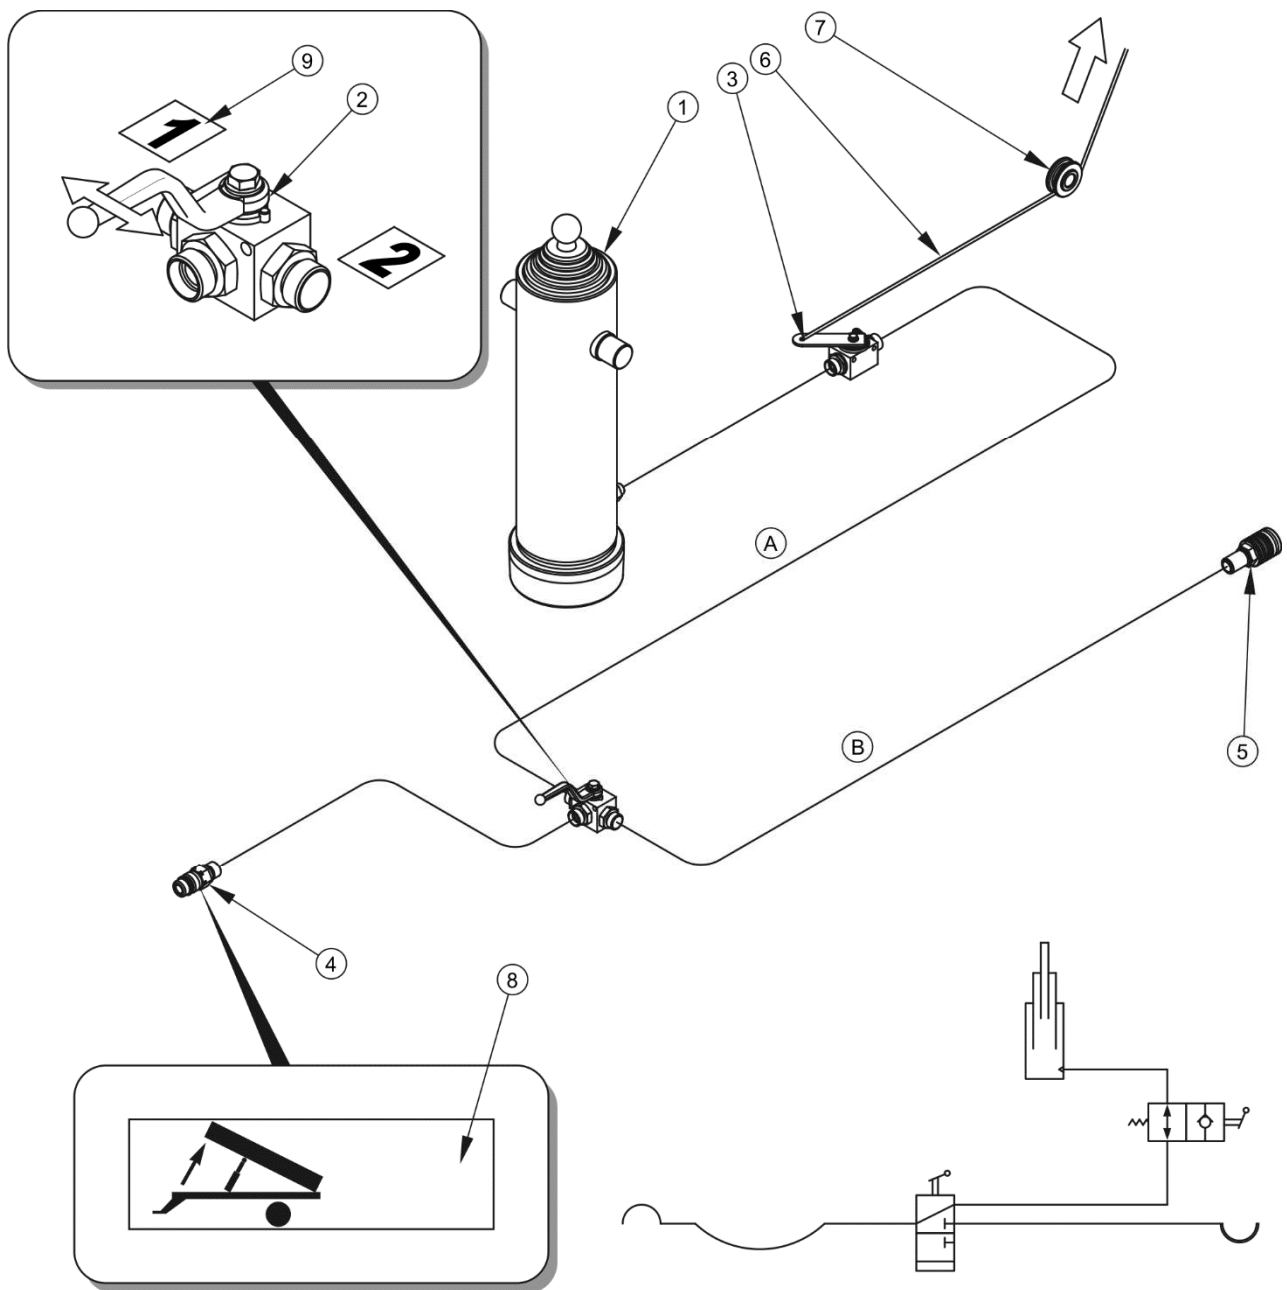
Construction et schéma de l'installation hydraulique du dispositif de basculement
